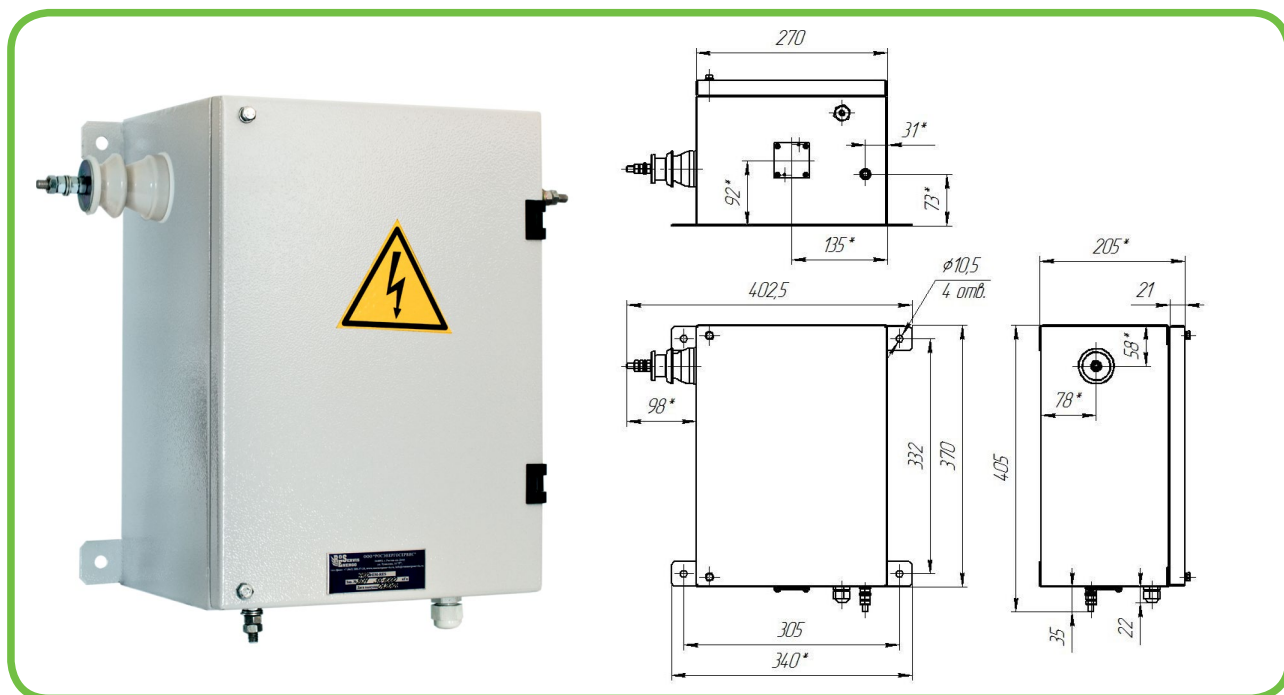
Общий вид и габаритные размеры фильтра присоединения ФПМ-Рс
